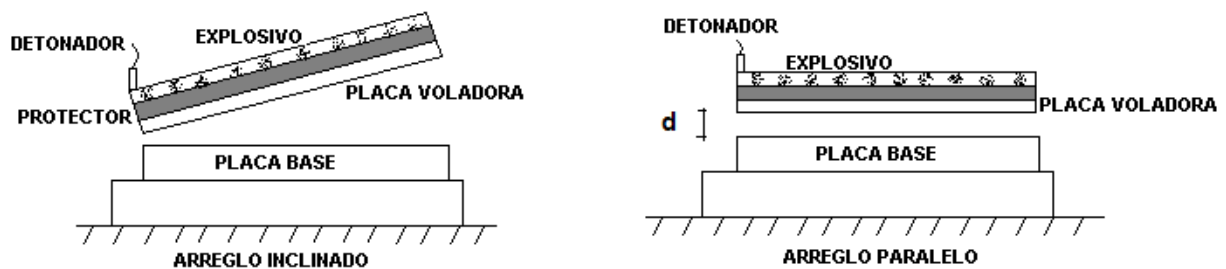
Arreglos para lograr Soldadura por Explosión
